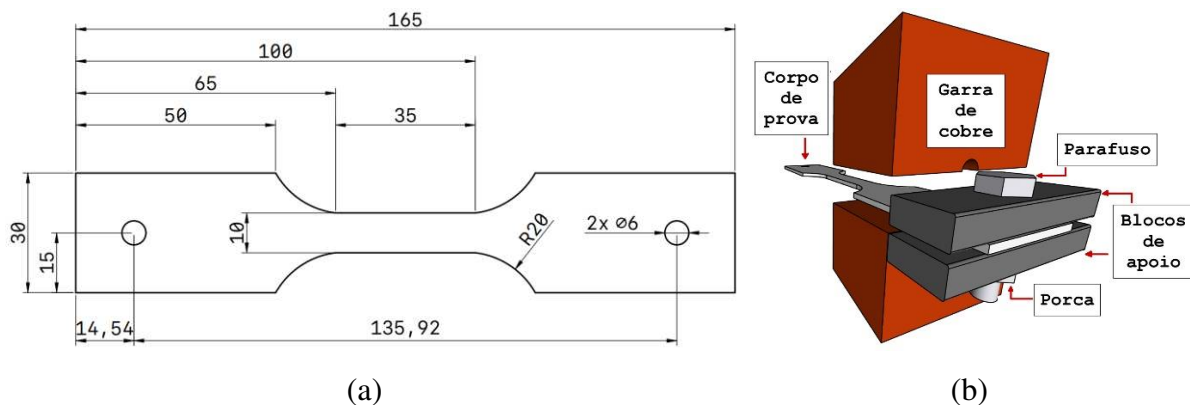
Geometria adotada do corpo de prova de tração uniaxial e esquema de montagem: (a) desenho técnico com dimensões em mm e (b) parte do sistema de fixação do corpo de prova.
